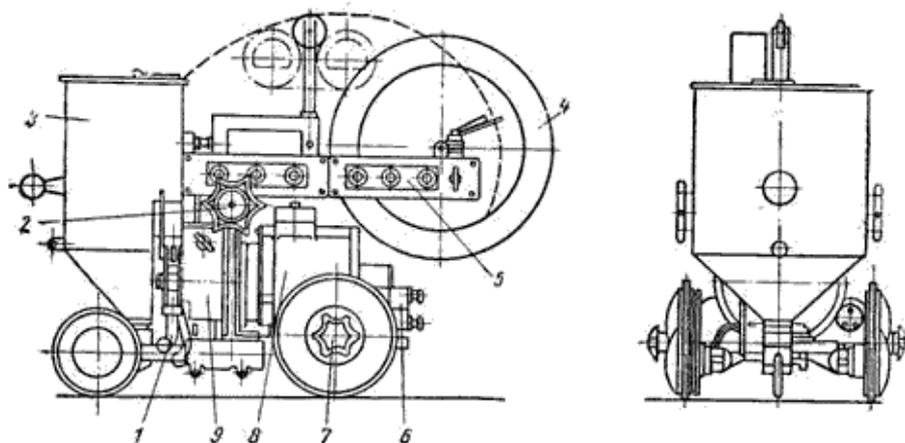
Трактор ТС-17М автомата для сварки под слоем флюса:
